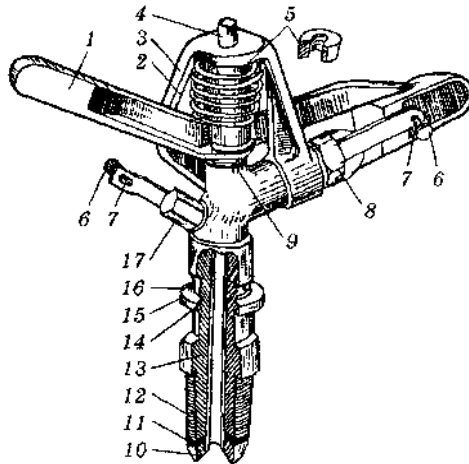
Далекоструминний дощувальний апарат з реактивною лопаткою:
